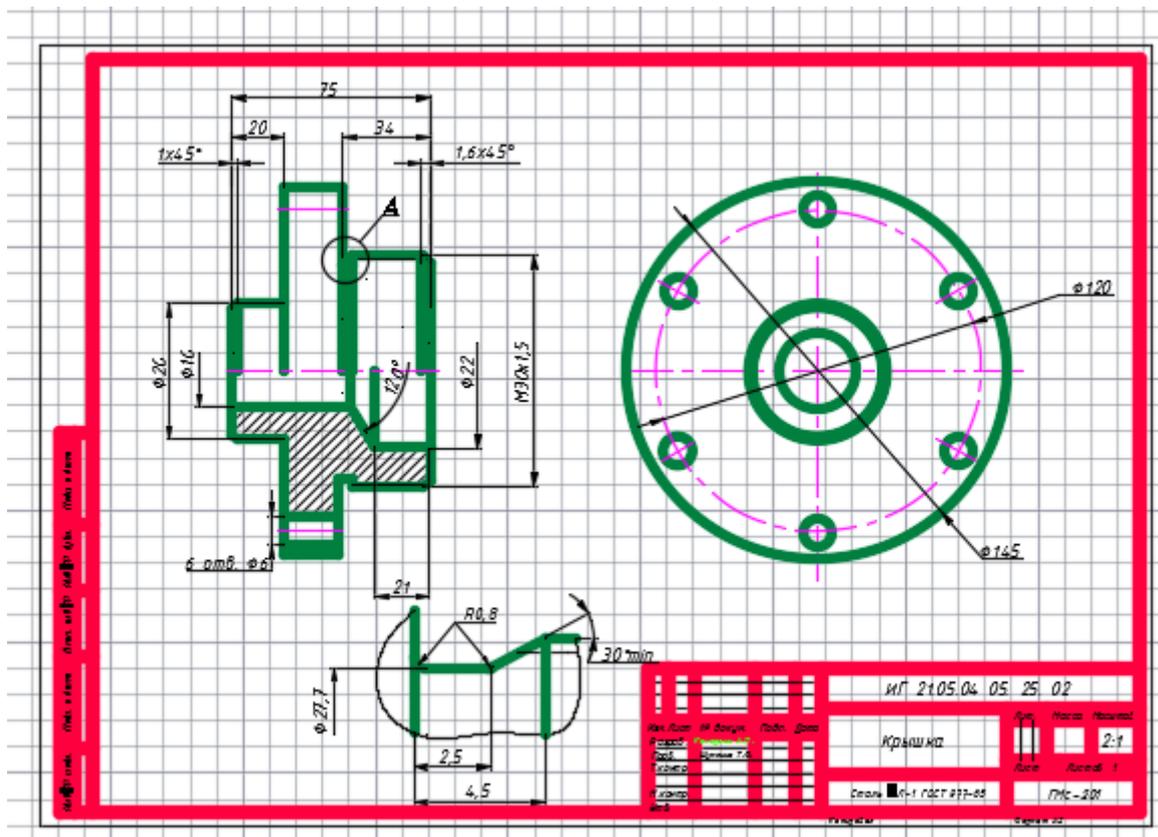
Рабочий чертеж крышки по стандартам ЕСКД
